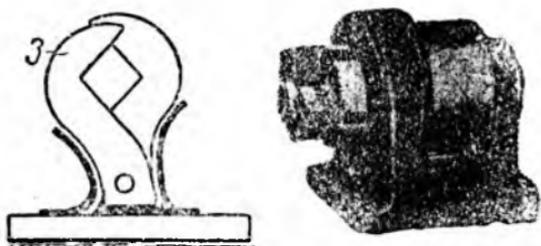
Короткий круглопалочный станок (справа) и механизм для направления подачи рейки (слева)
